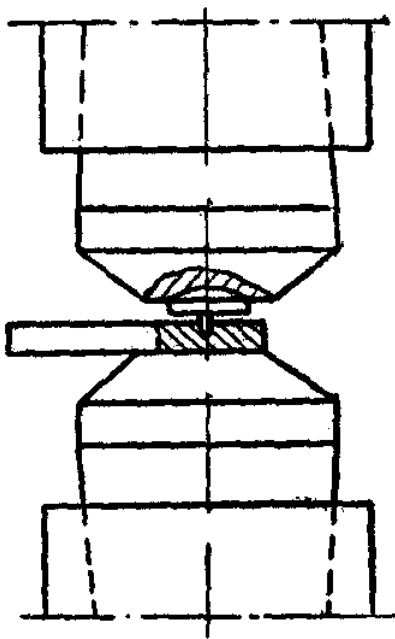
З'єднання деталей при контактному зварюванні.
